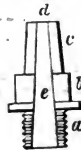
Der Zündkegel, wahre Größe. a das Gewinde; b der Fuß; c der Kegel; d die Schlagfläche; e die Zündröhre.
